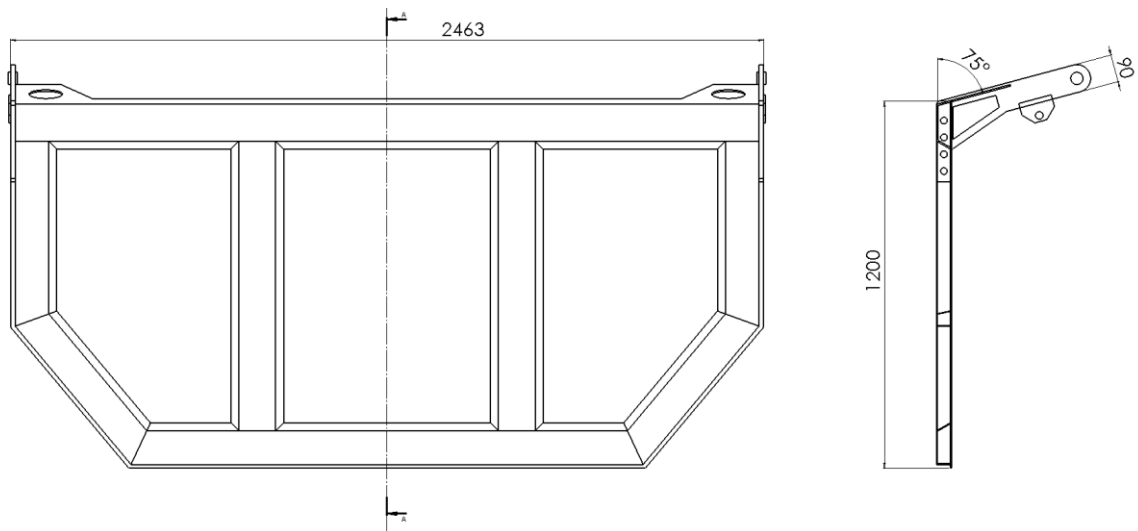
Porta hidráulica – Vista frontal e lateral em corte – cotas
